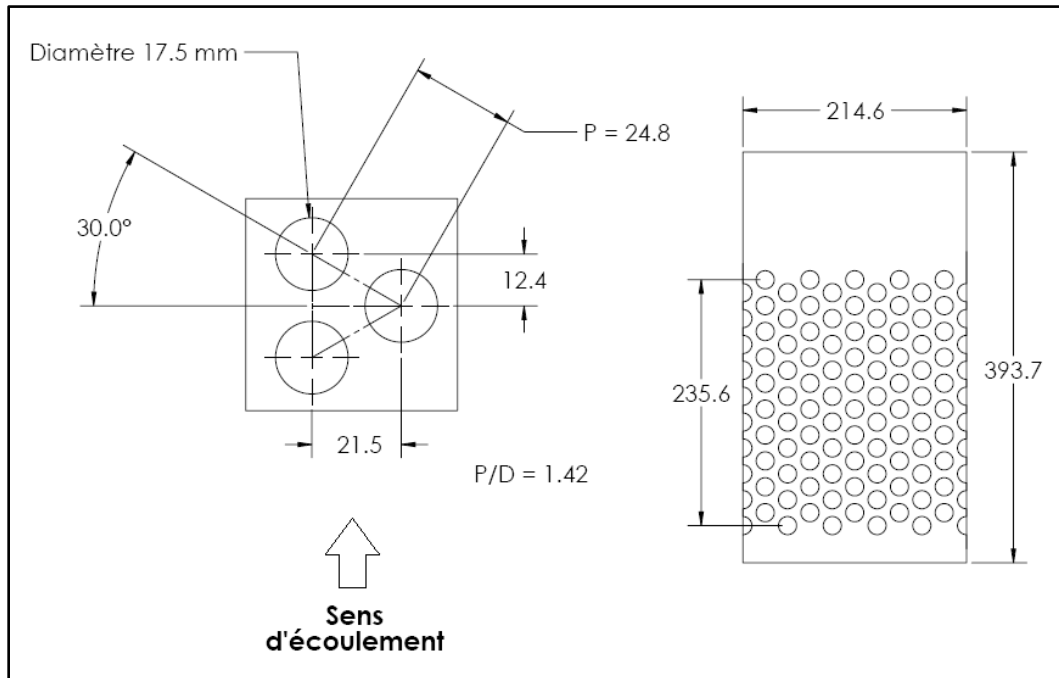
Dimensions et détails de la configuration de la section d'essai (les dimensions sont exprimées en mm)
